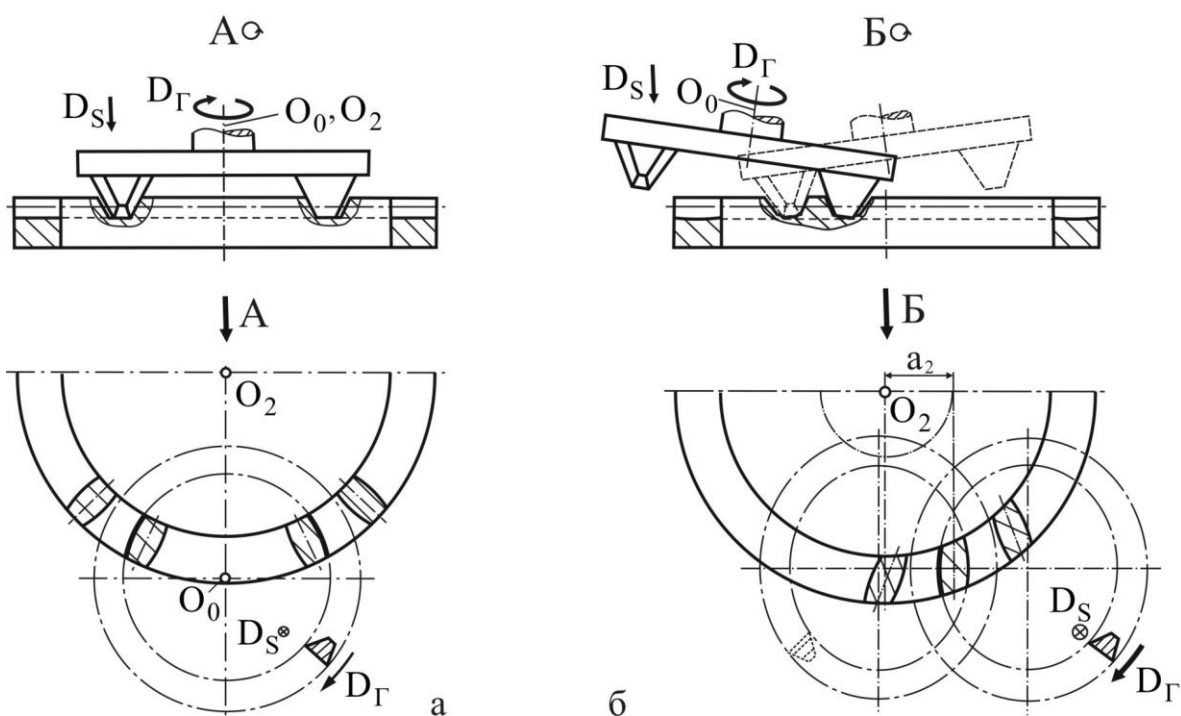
Схемы обработки плоского колеса торцовой зуборезной головкой
